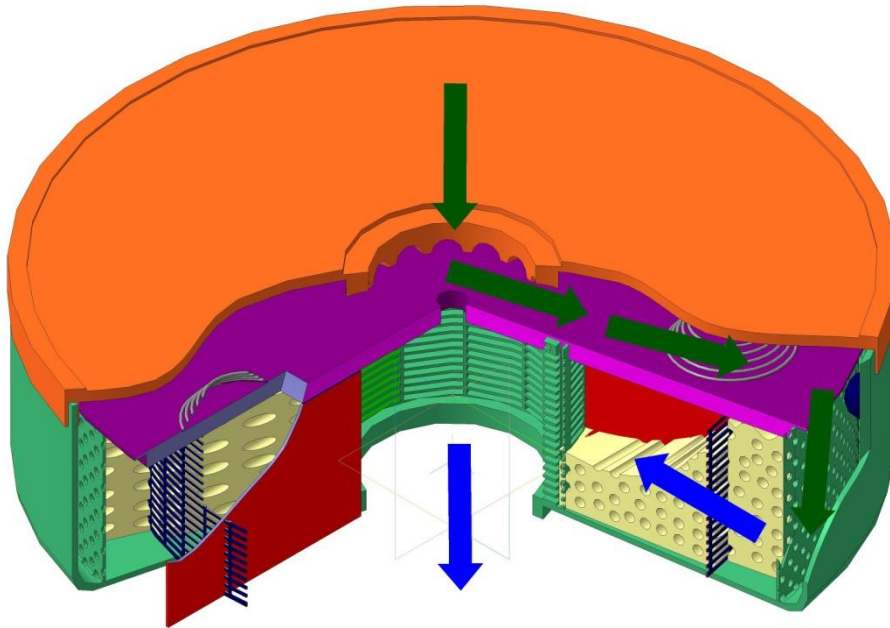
Регенеративный патрон с центростремительным движением воздуха
